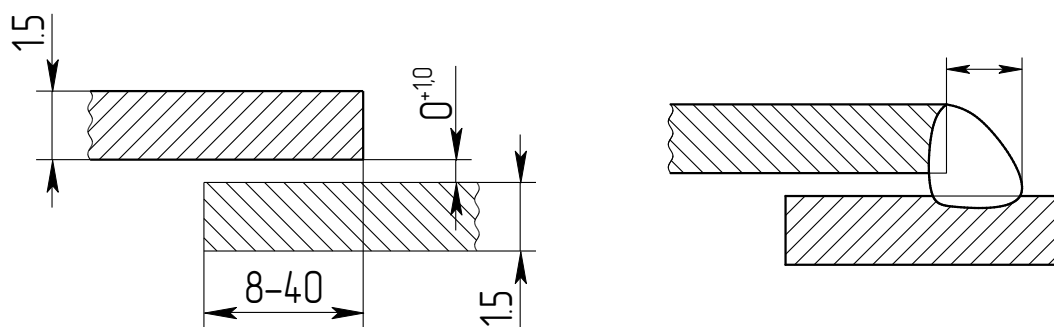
Конструктивные элементы сварного соединения Н1
